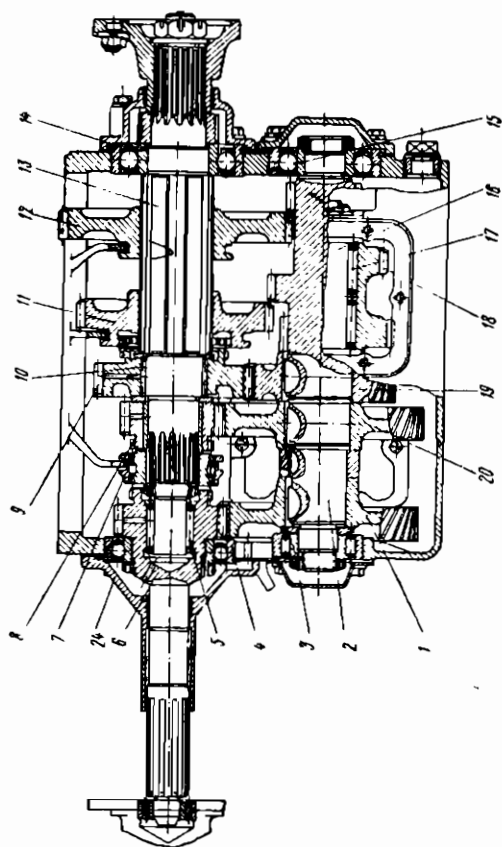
Коробка перемены передач (разрез и вид с торца):
